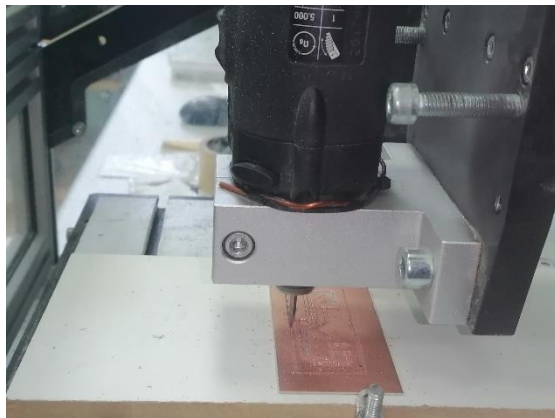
Изготовление печатной платы на станке с ЧПУ
